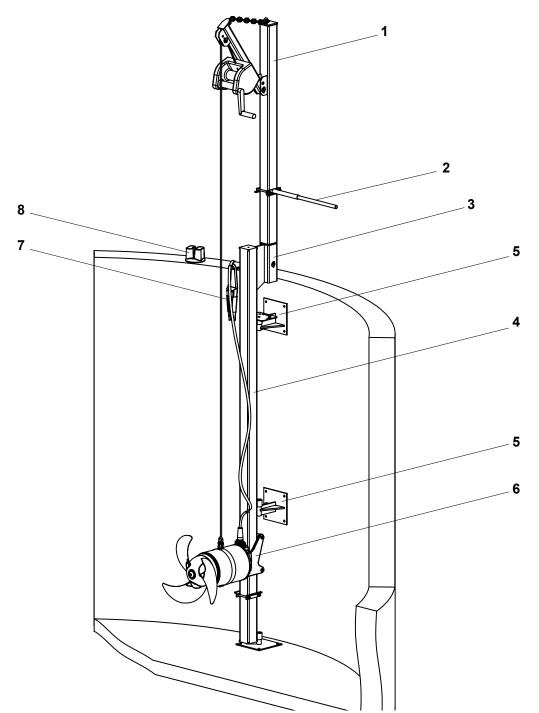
Esempio di installazione con altre possibilità di fissaggio
